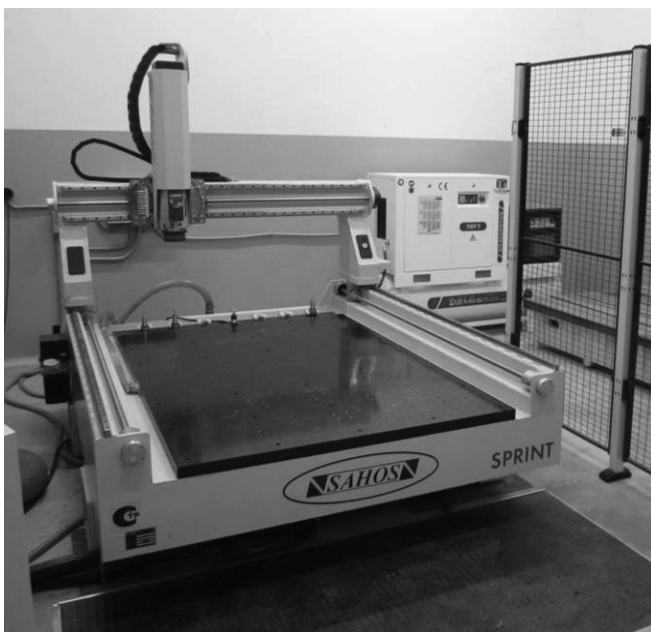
Фрезерный станок с ЧПУ SPRINT FC1900CNC
